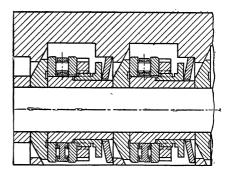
Установка упорных роликоподшипников в коробках приводов двух червячных прессов
